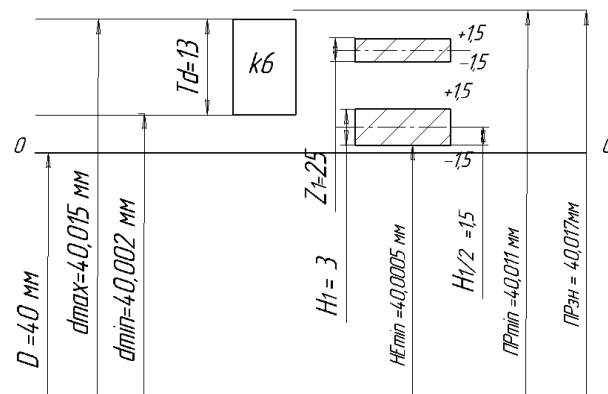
Схема розташування полів допусків для розміру Ø40k6
